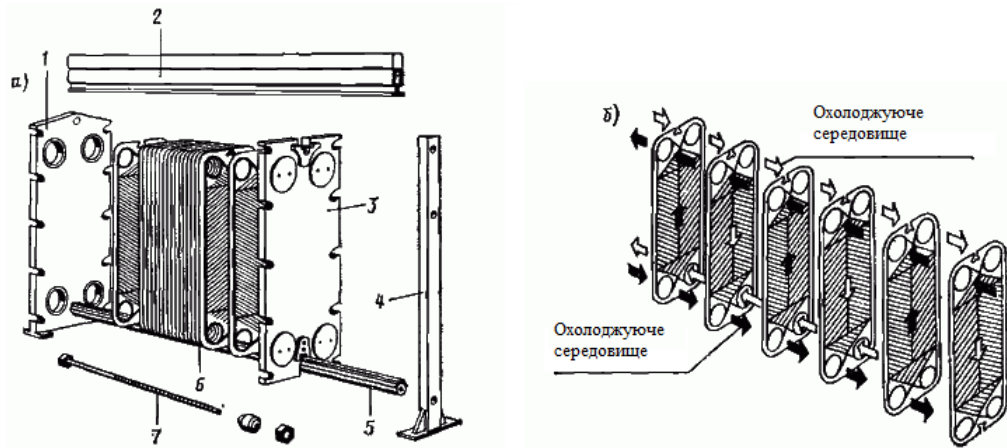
Охолоджувач мастила: *а* – пристрій; *б* – напрям руху охолоджуючого та охолоджуваного середовищ; 1 – нерухома плита; 2 – верхня направляюча штанга; 3 – рухома плита; 4 – опорна стійка; 5 – нижня направляюча штанга; 6 – пакет пластин; 7 – стяжний болт
